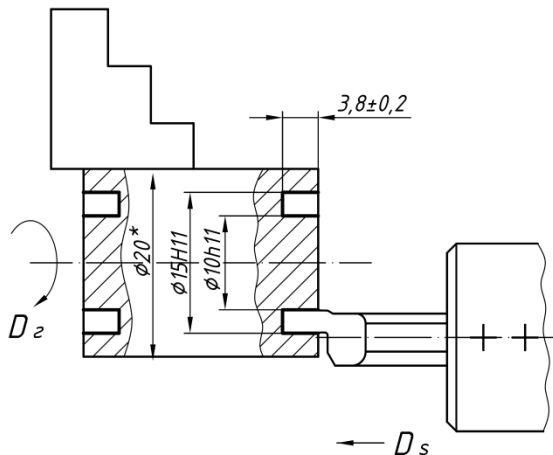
Операционный эскиз обработки торцевой канавки. Материал заготовки – 12Х18Н10Т.
